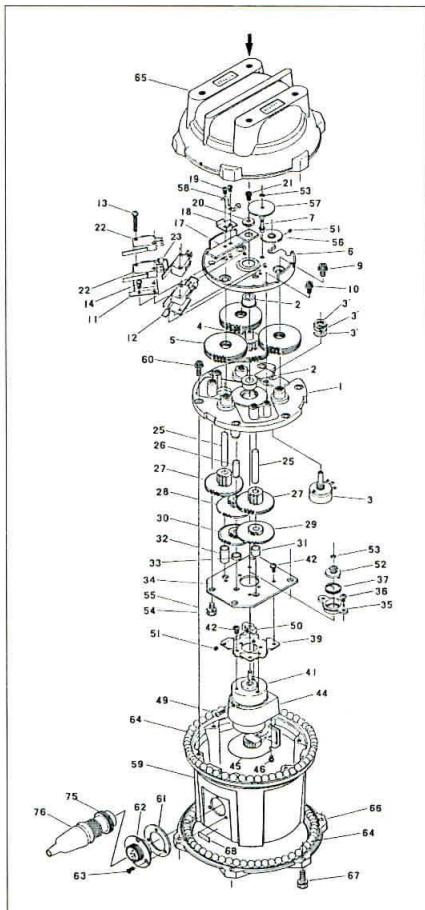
Para los curiosos, he aquí una vista en explosión del despiece del rotor. Es una impresionante red de ferretería en un pequeño espacio y es por ello que hace un gran trabajo.
